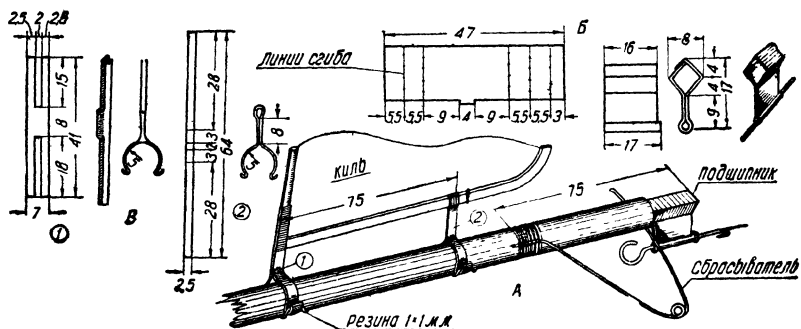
Конструкция подшипника, сбрасывателя и крепления килля:
